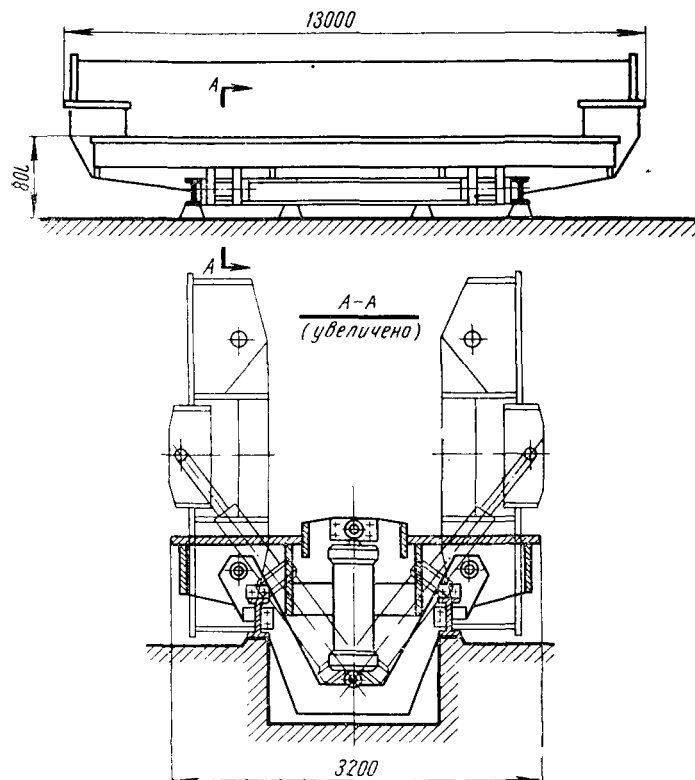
Кантователь-кондуктор с гидроцилиндрами
